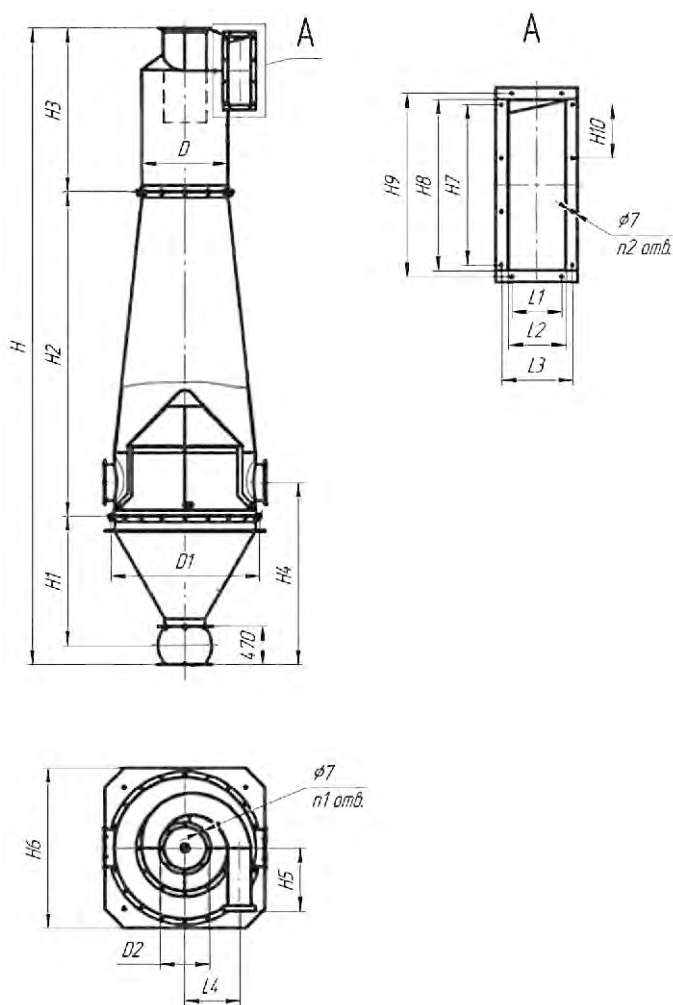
Габаритные и присоединительные размеры циклона ЦМ.
